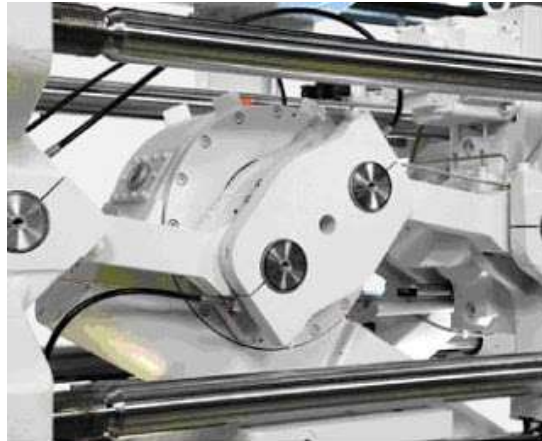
Sistema de cierre a rodillera tipo Z. [5]
